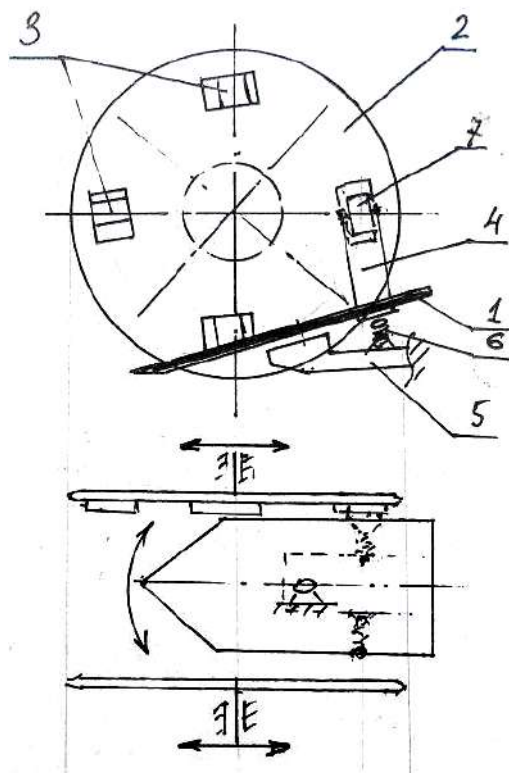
Схема предлагаемой конструкции подкапывающего органа
